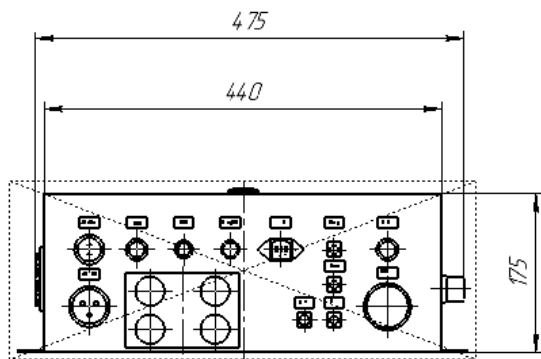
Габаритные и присоединительные размеры БКВИП
